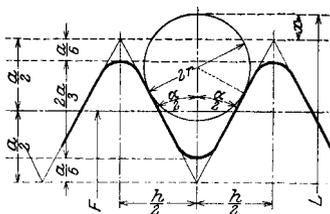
Gewindemessung mittels kalibrierter Drähte.
